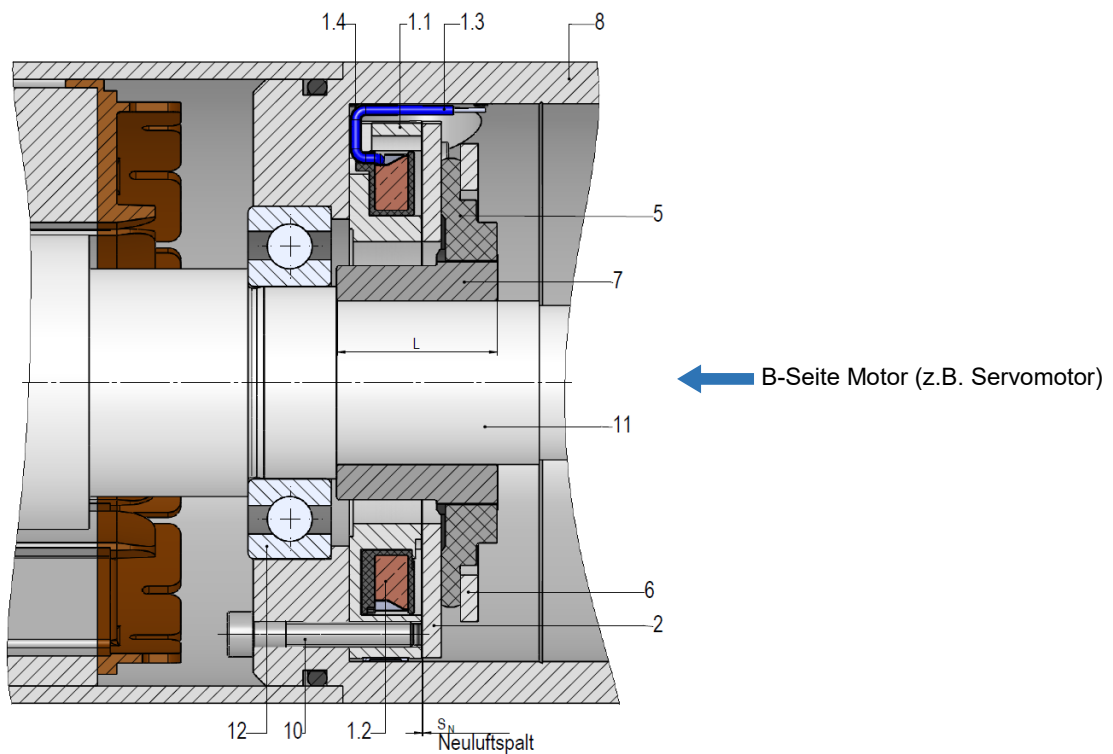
/2: Stirnseitiger Befestigung am Beispiel der Federdruck-Einscheibenbremse SL 502..A00 in den Motor (z.B. Servomotor) mit Anschlag des Mitnehmers (7) an der Anschlagshulter der Motorwelle (11) und Verbindung des Mitnehmers (7) mit der Motorwelle (11) durch Presspassverbindung (siehe Kapitel 4.1.2)
